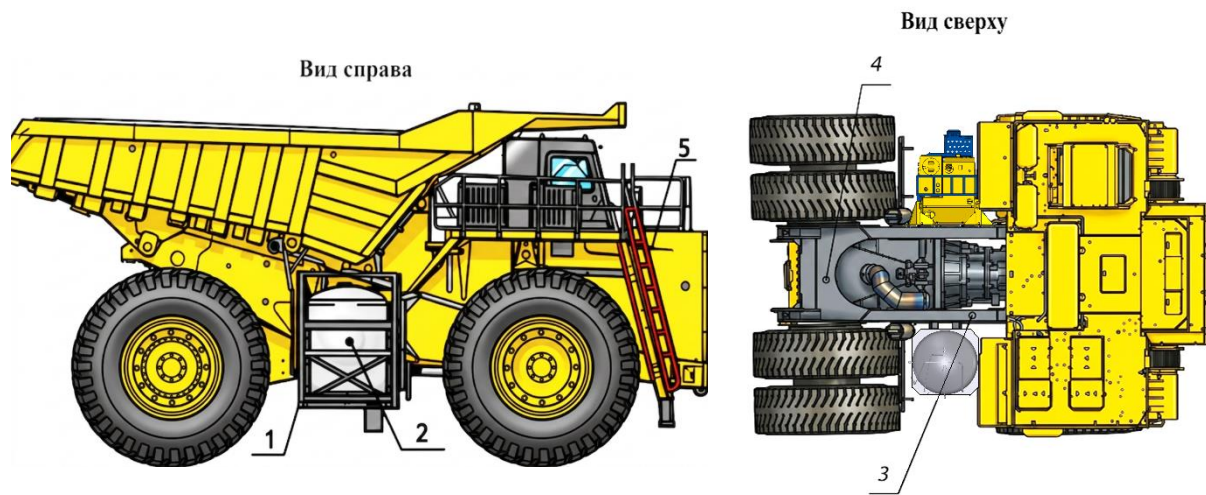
Компоновка криогенного топливного оборудования на раме БелАЗ-75306 (1 - опорная платформа; 2 - криогенный топливный бак (КТБ); 3 – правый лонжерон; 4 - несущая рама; 5 - карьерный самосвал БелАЗ-75306).
